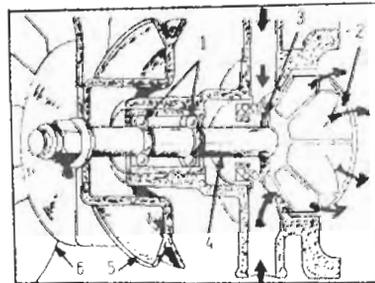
Sección de la bomba de agua. 1.- Rodamientos de bolas. 2.- Rodete. 3.- Retén. 4.- Eje. 5.- Polea para la correa de transmisión. 6.- Ventilador.
